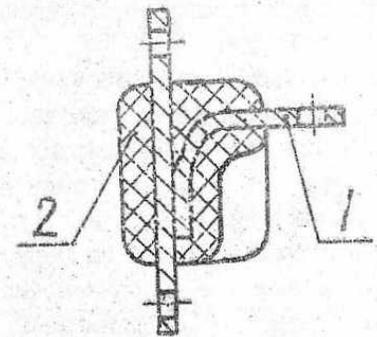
Изображение сложного изделия: 1 - сборочная единица; 2 - корпус
